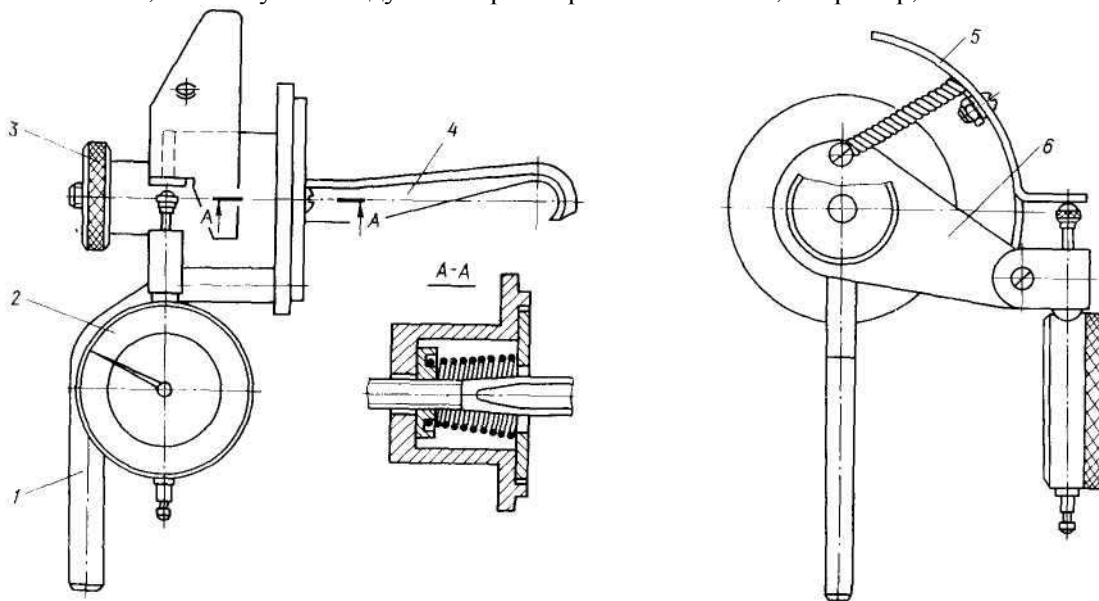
Контрольное приспособление для проверки зазора в шестернях главной передачи:
